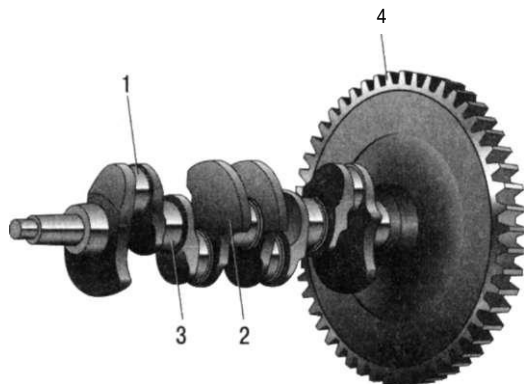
Устройство коленчатого вала двигателя: 1 - шатунная шейка; 2 - противовес; 3 - коренная шейка; 4 - маховик
